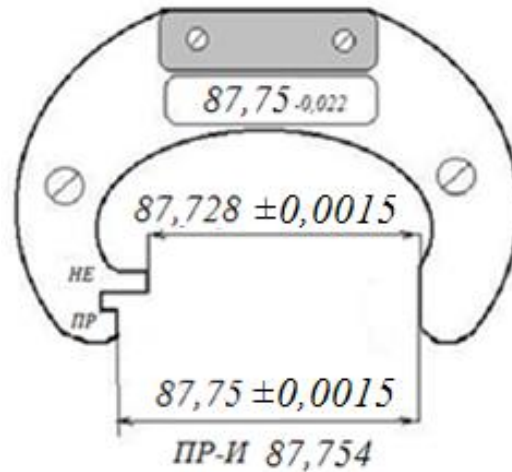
Эскиз калибра-скобы из современных износостойких материалов для контроля размера шатунной шейки коленчатого вала двигателей ЯМЗ после шлифовки под ремонтный размер $87,75_{-0,022}$
